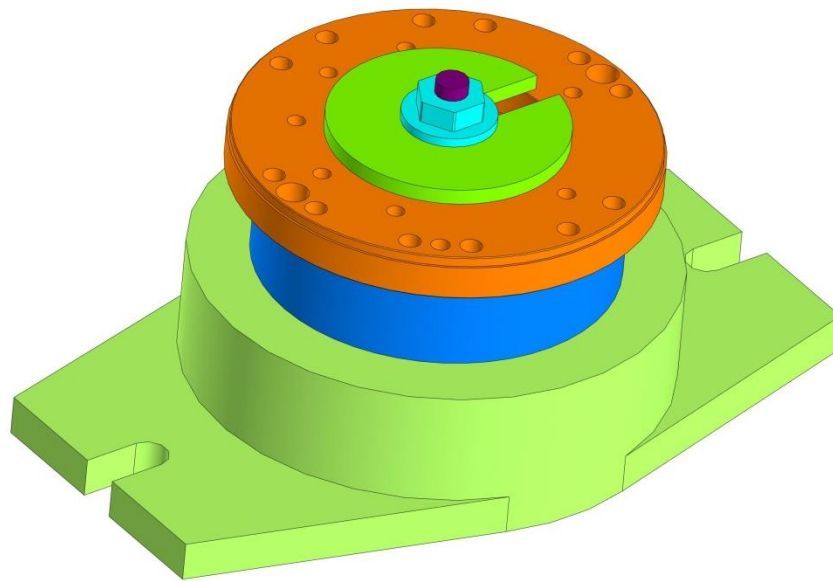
Спроектований верстатний пристрій та закріплена деталь
